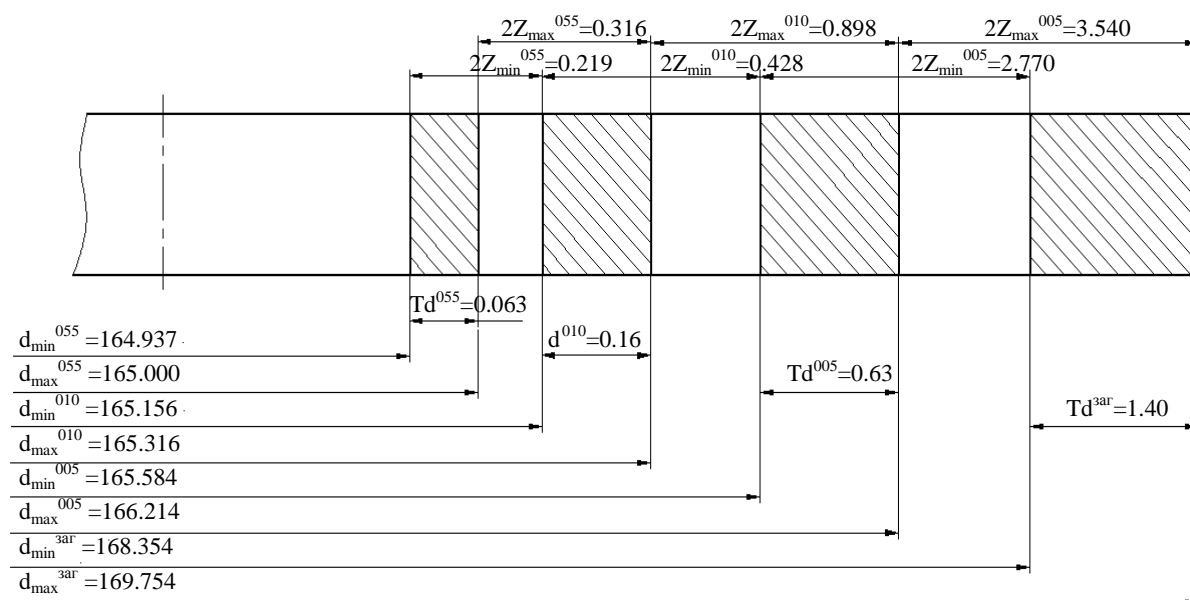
Схема расположения припусков, допусков и операционных размеров на шейку $\varnothing 165h8_{(-0,063)}$
